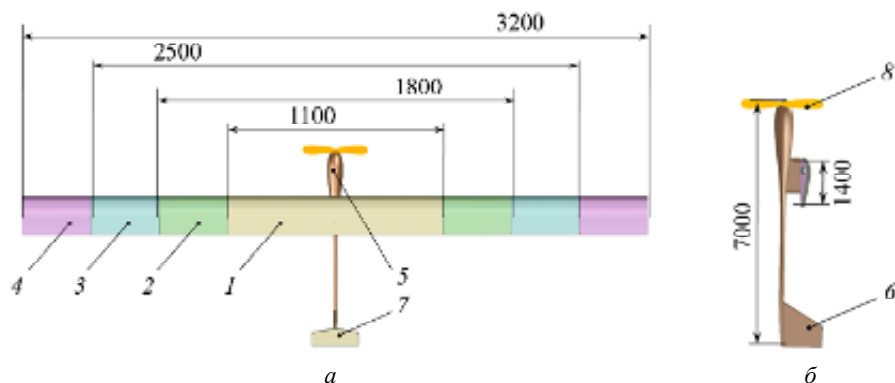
Габаритный и компоновочный эскиз самолета с раздвижным крылом: а – вид сверху; б – вид сбоку
